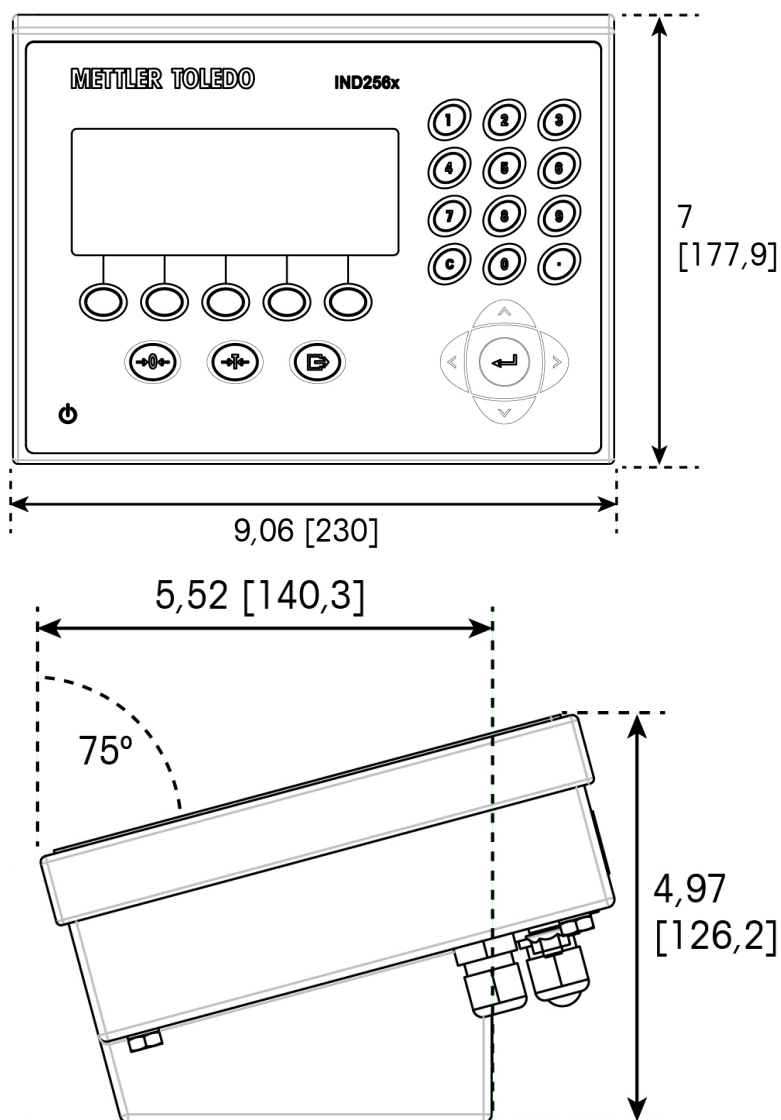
Dimensões do IND256x, Instalação em Bancada
